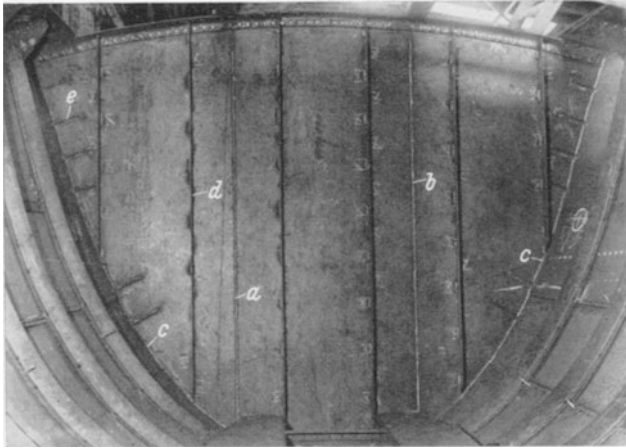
Geschweißtes Kollisionsschott eines Motorschiffes.
